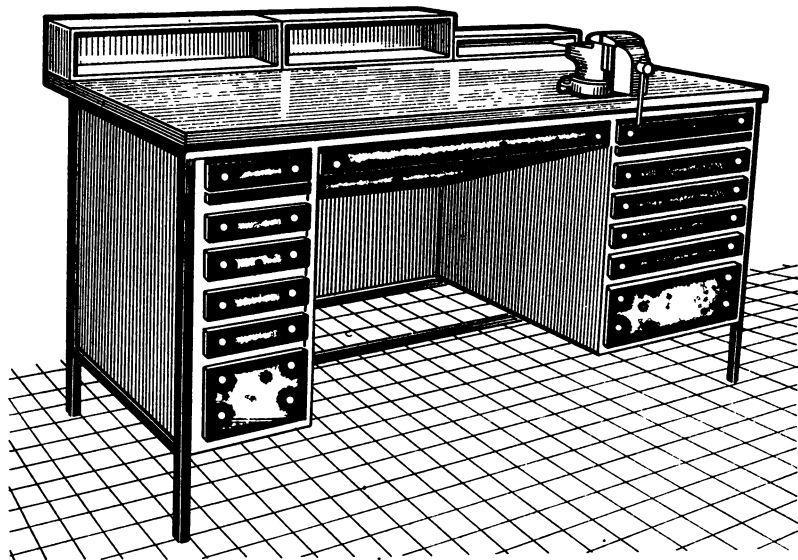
Слесарно-сборочный верстак. Материал — фанерованная столлярная плита, листовой алюминий, стандартная стальная труба квадратного сечения. Каркас стола цельносварной, остальные элементы сборно-разборные
